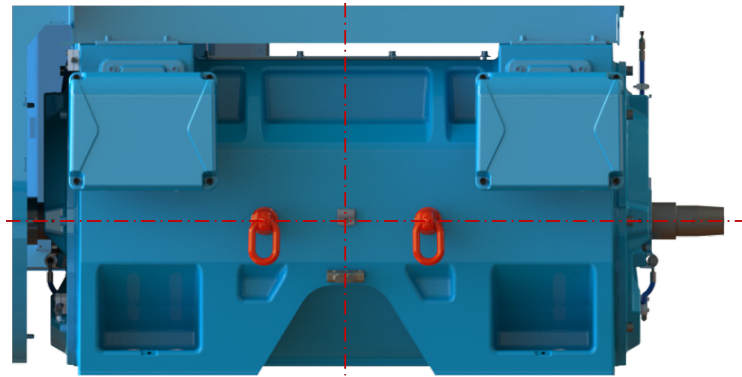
Detalle de la posición para fijación del dispositivo del sistema WEG Motor Scan en los motores W60
